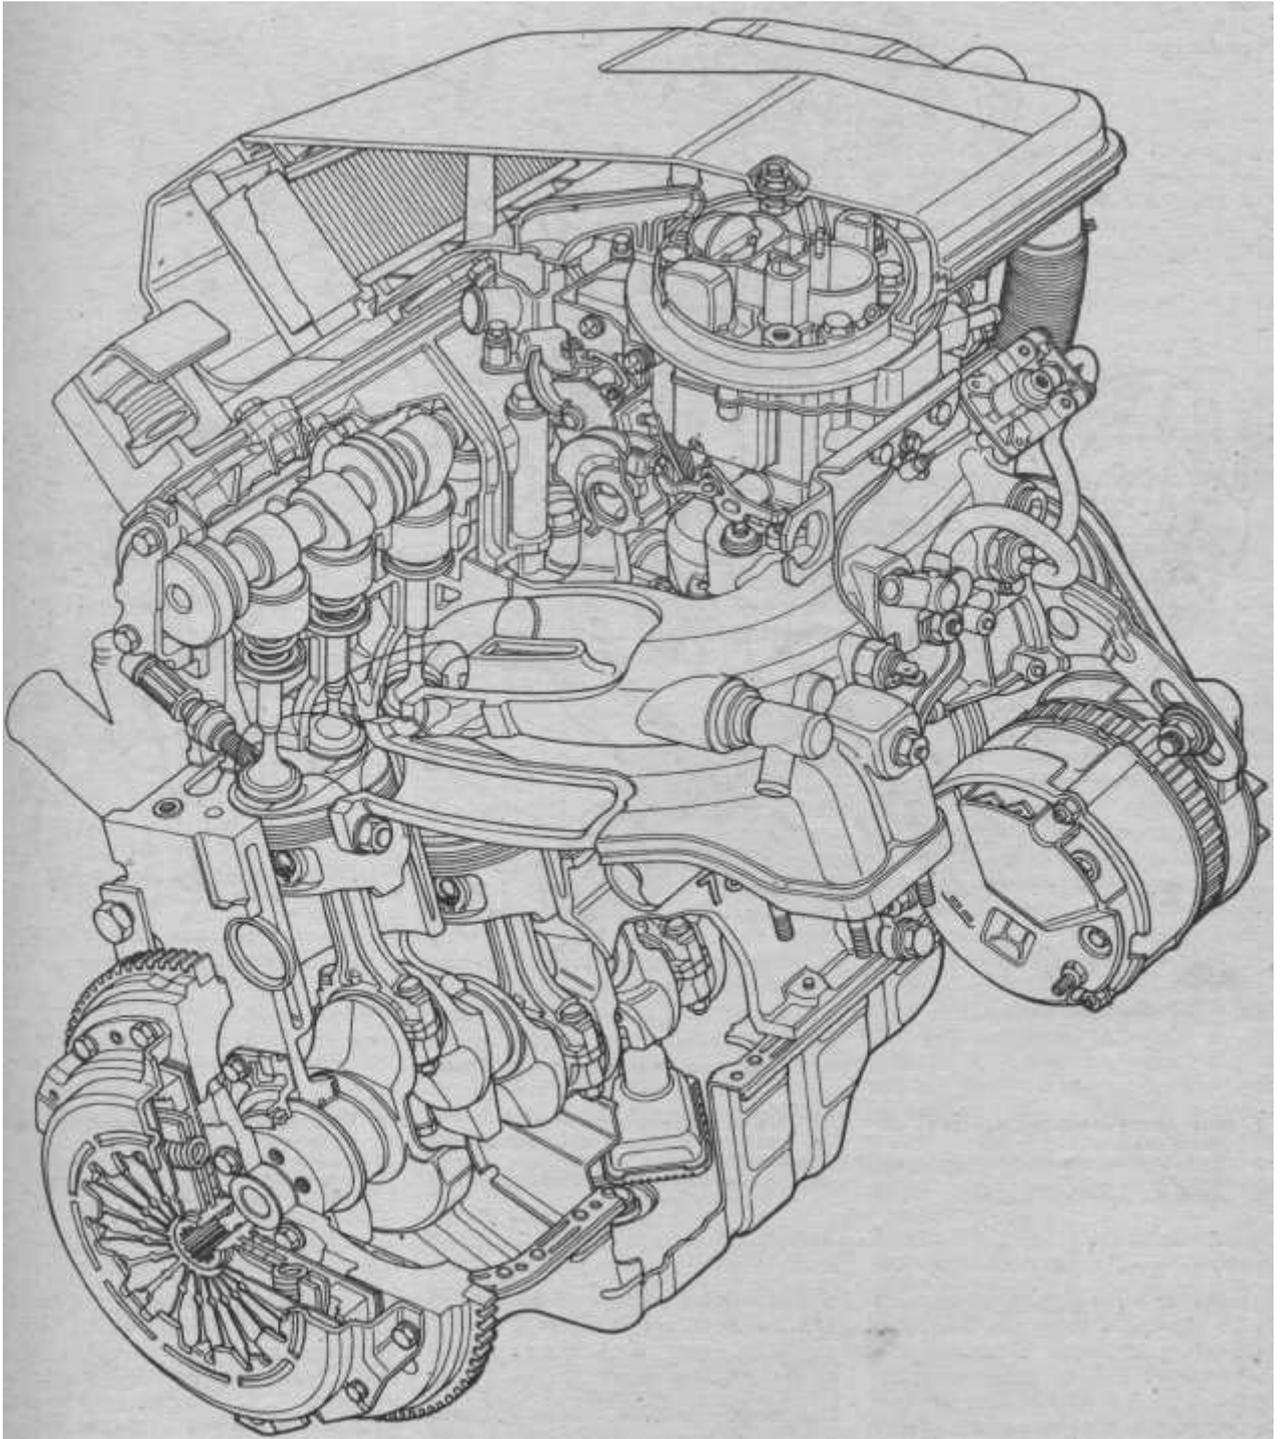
Общий вид двигателя 1.4 л (Глава 1)
